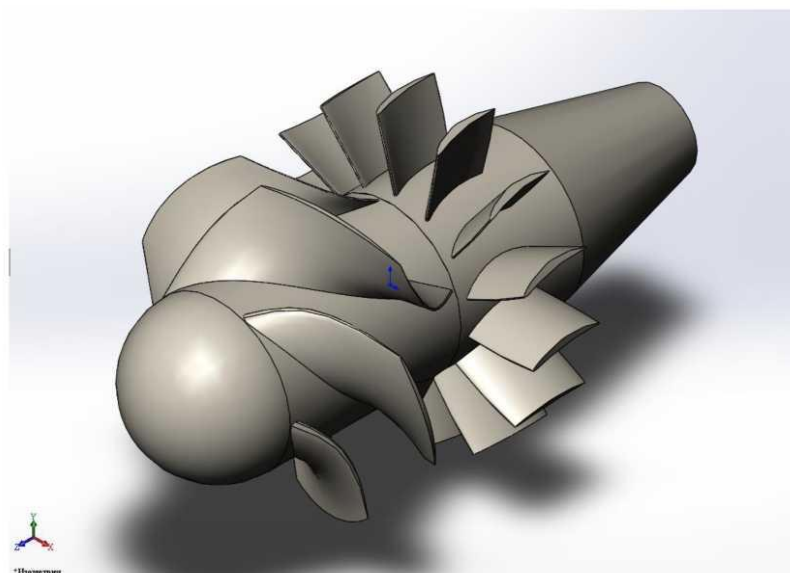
Твердотільна 3Б-модель лопатевої системи
